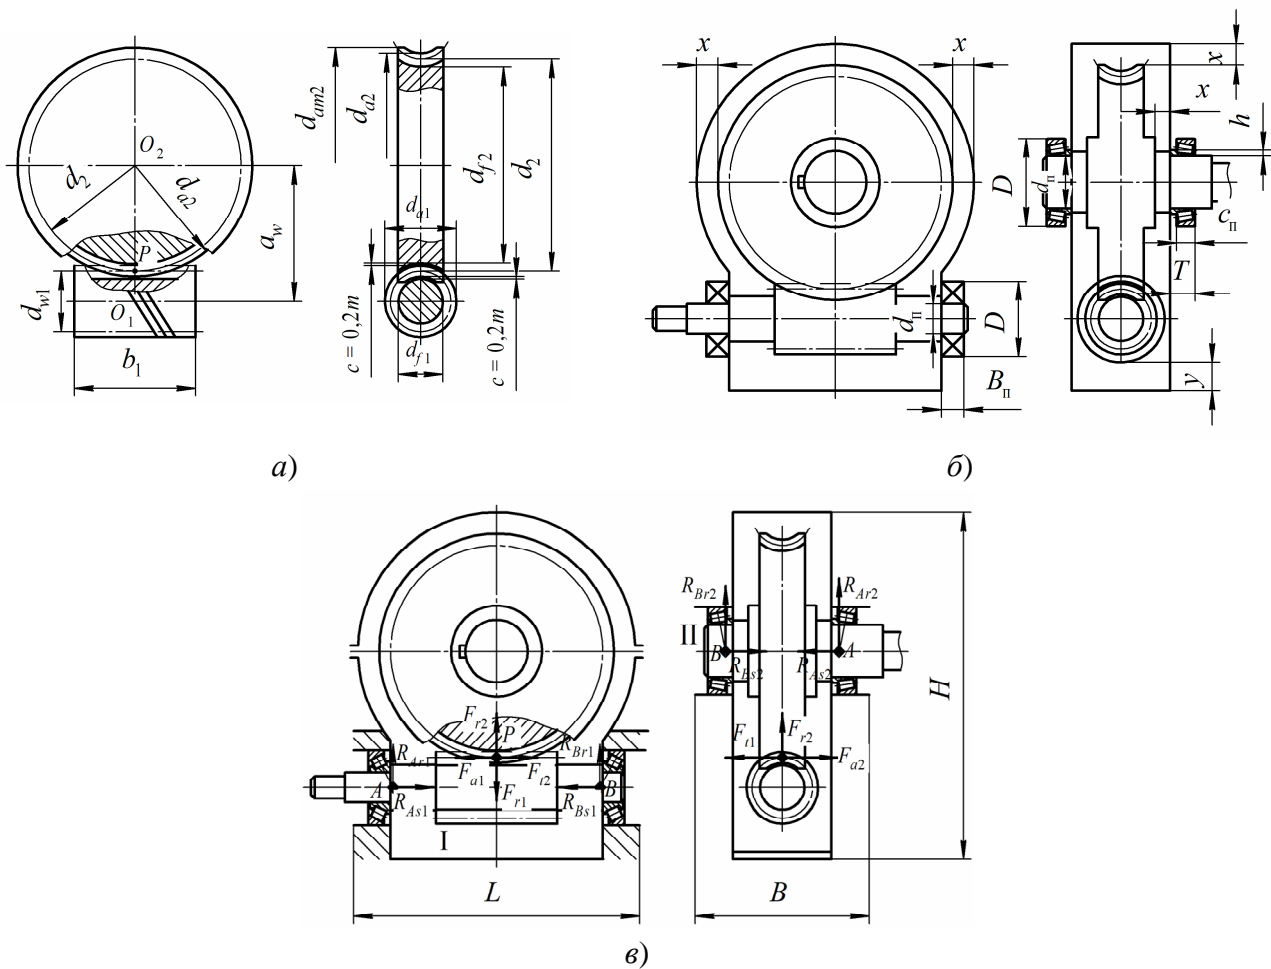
Последовательность вычерчивания эскизной компоновки червячного редуктора
